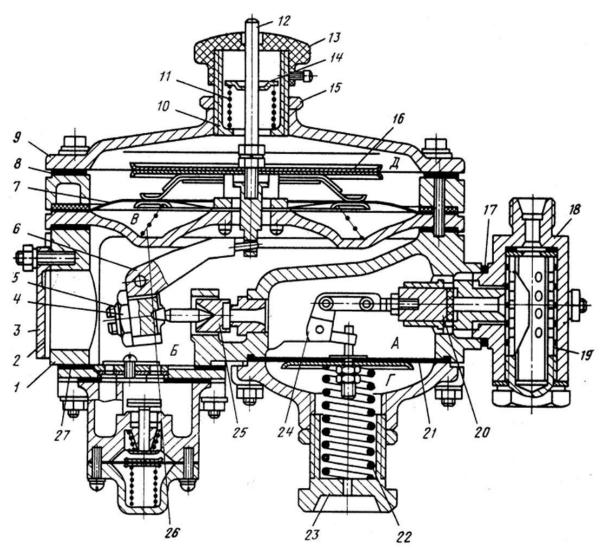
Газовый редуктор низкого давления: А - полость первой ступени: Б - полость второй ступени; В - полость разгрузочного устройства; ГиД полости атмосферного давления; 1 - корпус газового редуктора; 2 прокладка; 3 - крышка; 4 - контргайка регулировочного винта; 5 регулировочный винт клапана низкого давления; 6 - рычаг диафрагмы низкого давления; 7 - разгрузочная диафрагма; 8 - прокладка разгрузочной диафрагмы; 9 - крышка корпуса верхняя; 10 - седло пружины диафрагмы низкого давления; 11 - пружина диафрагмы низкого давления; 12 - шток диафрагмы низкого давления; 13 - регулировочный ниппель пружины; 14 шайба упорная пружины; 15 - контргайка седла; 16 - диафрагма низкого давлени; 17 - прокладка корпуса фильтр; 18 - фильтр газового редуктор; 19 - сетка фильтр; 20 - клапан высокого давления; 21 - диафрагма высокого давления; 22 - пружина диафрагмы высокого давления; 23 регулировочная гайка пружины; 24 - рычаг клапана высокого давления; 25 - клапан низкого давления; 26 - пружина разгрузочного устройства; 27 пластина и прокладка пластины.
